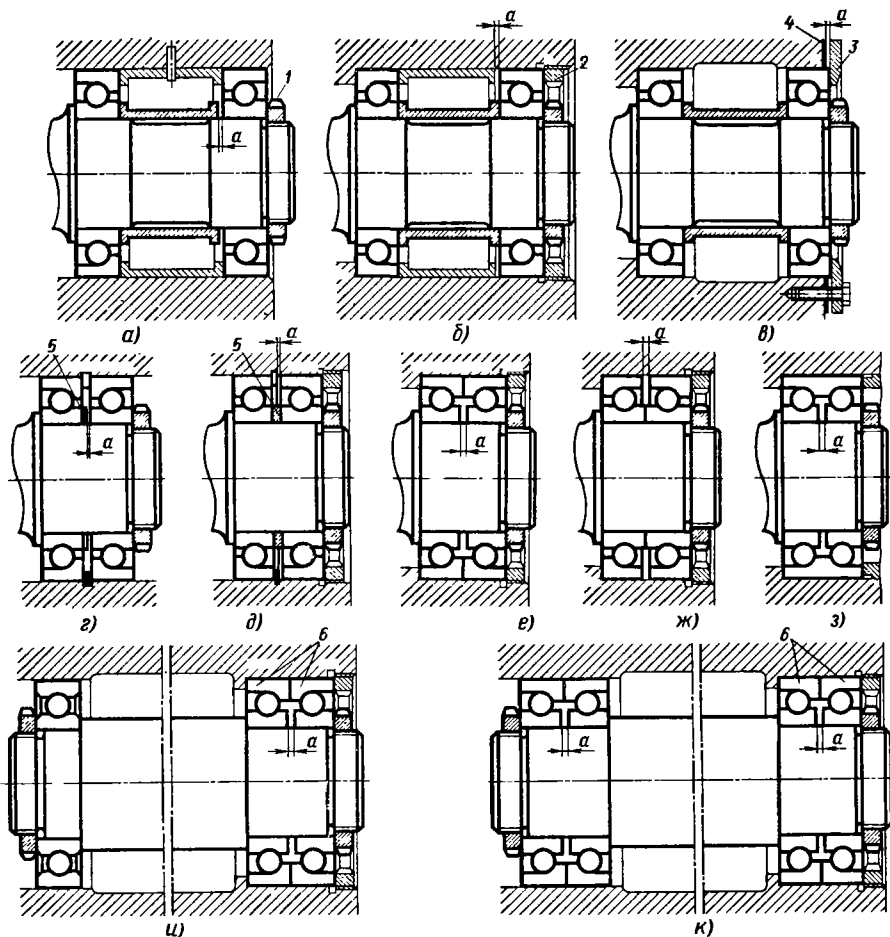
Установка радиально-упорных подшипников с предварительным натягом
